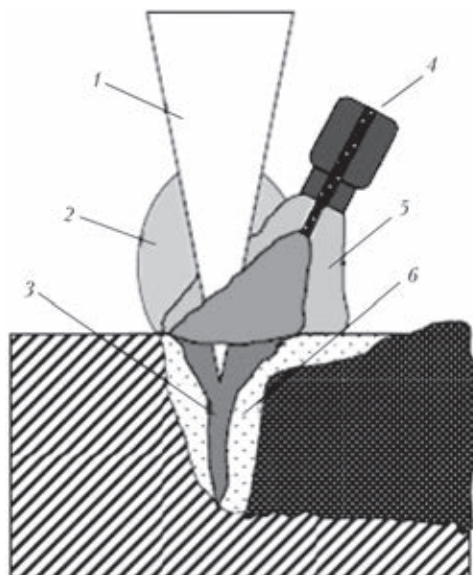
Схема гибридной лазер-МИГ сварки [3]: 1 — лазерное излучение; 2 — лазерная плазма; 3 — парогазовый канал; 4 — дуга плавящегося электрода; 5 — защитный газ; 6 — сварочная ванна
